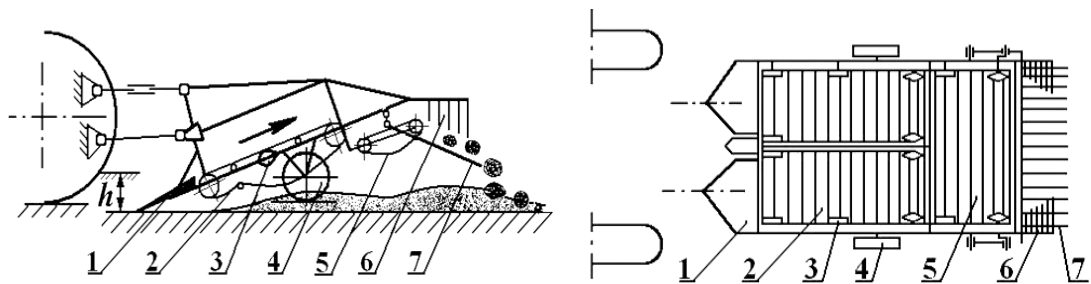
Схема елеваторного копача: 1 – леміш; 2 – основний прутковий елеватор; 3 – струшувач; 4 – опорне колесо; 5 – каскадний елеватор; 6 – звужувальний щиток; 7 – струшувальна решітка
